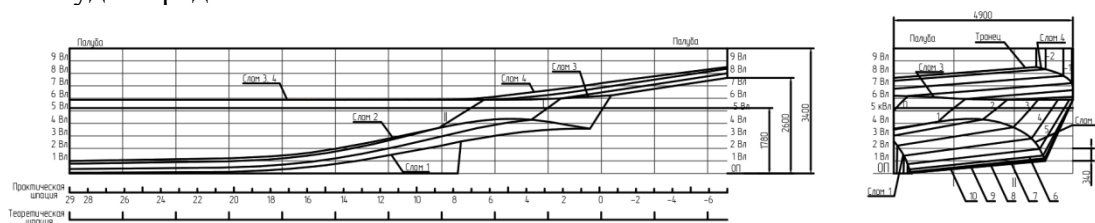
Форма корпуса парома шифра «ЭКО-Паром»
